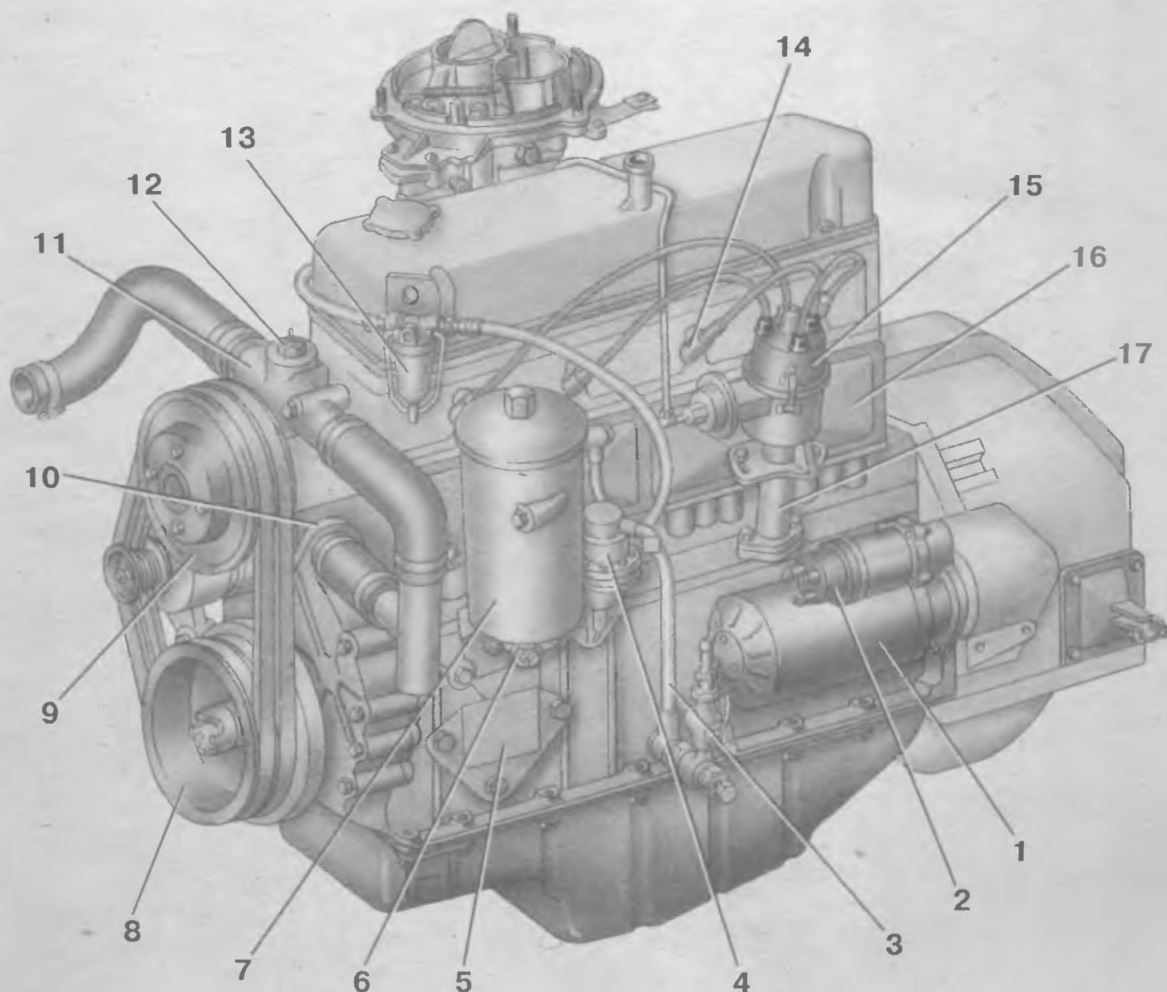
Вид двигателей мод. 402 и 4021 с левой стороны: 1 – стартер; 2 – тяговое реле стартера; 3 – маслопровод; 4 – топливный насос; 5 – кронштейн опоры двигателя; 6 – датчик лампы аварийного давления масла; 7 – масляный фильтр; 8 – шкив коленчатого вала; 9 – шкив водяного насоса; 10 – водяной насос; 11 – термостат; 12 – датчик указателя температуры охлаждающей жидкости; 13 – фильтр тонкой очистки топлива; 14 – свеча зажигания; 15 – распределитель зажигания; 16 – крышка толкателей; 17 – привод распределителя зажигания и масляного насоса
